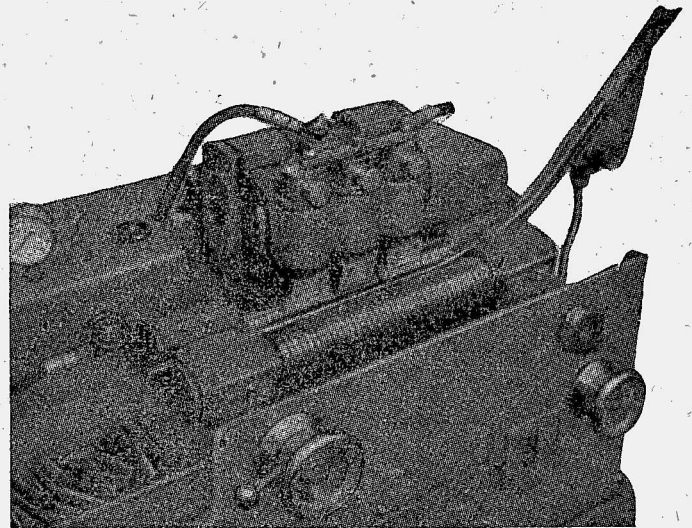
Konstrukcja urządzenia do doglądania wg schematu z rys. 8 opracowana przez P. E. Djaczenkę
